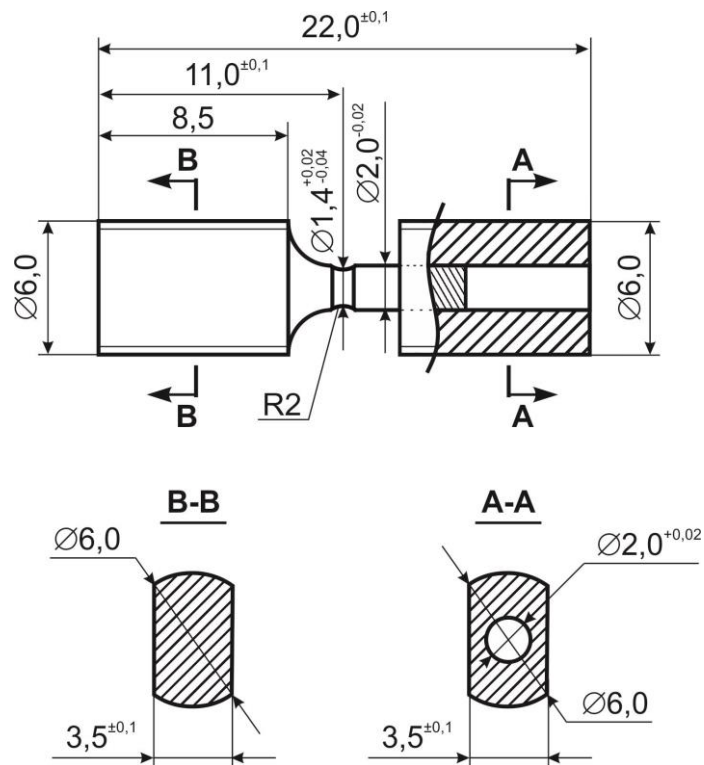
Составной образец в сборе для испытаний на ударный изгиб, изготовленный из испытанного образца для автоклавных испытаний на рисунке 2.4
